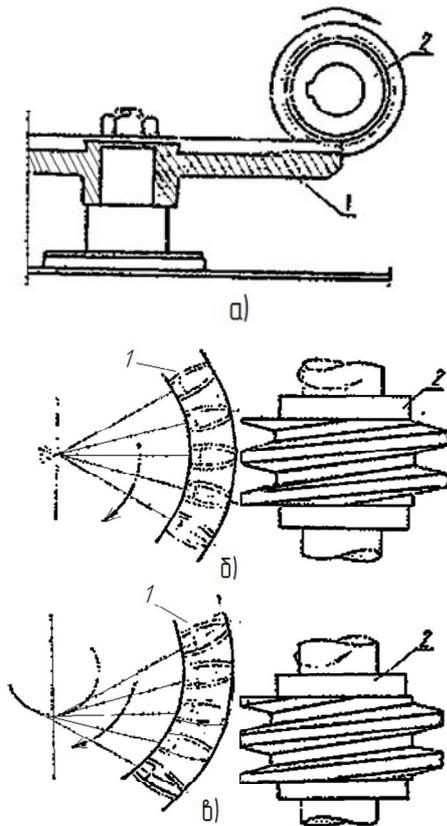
Способ нарезания плоских зубчатых колес цилиндрических передач методом обкатки на зуборезных станках: 1 – плоское колесо; 2 – фреза
